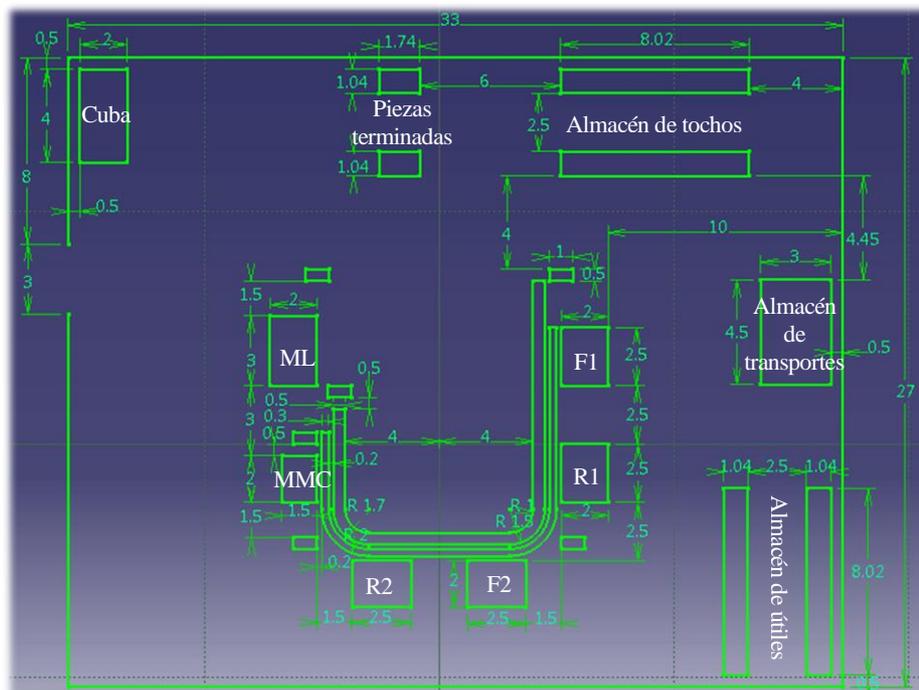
36. Layout final de la planta de fabricación. Fuente: Elaboración propia.
